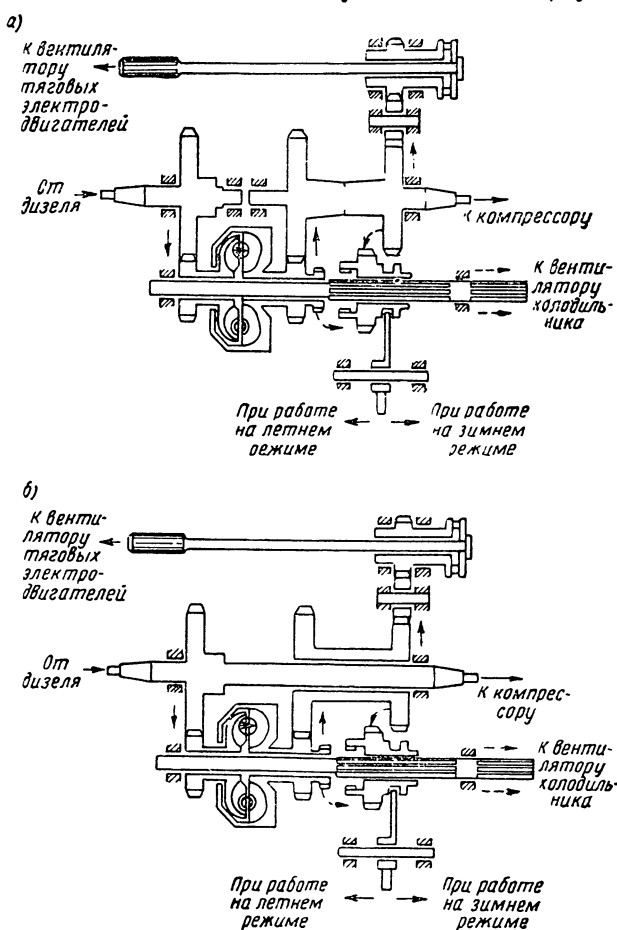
Схема работы гидромеханического (распределительного) редуктора:
